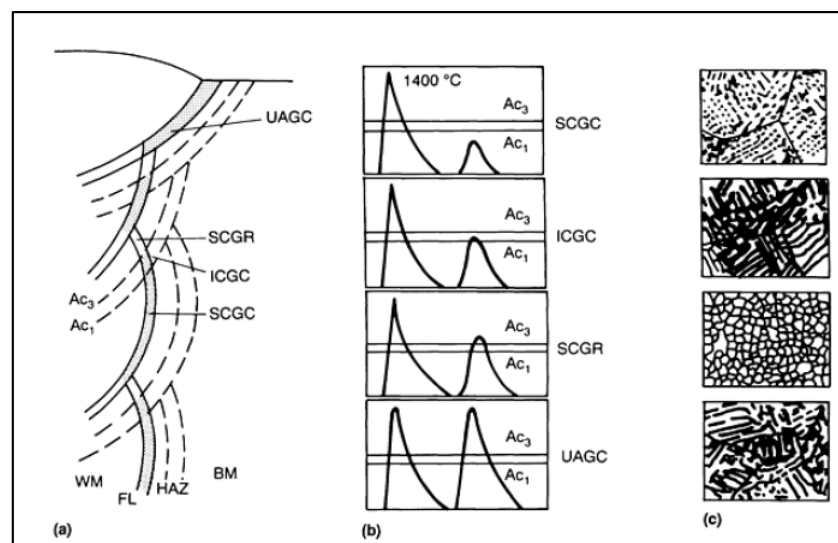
Transformaciones de grano a lo largo de la junta soldada.
